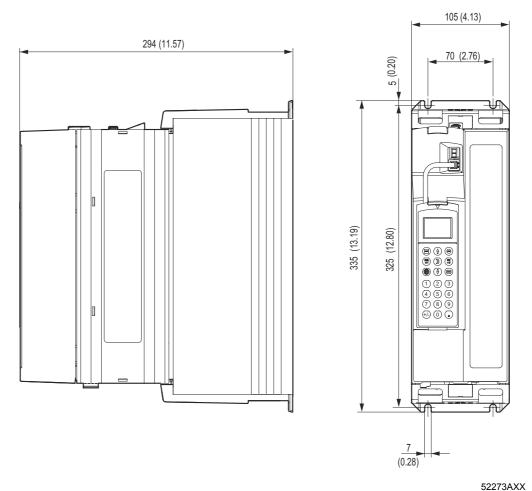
Dimensões MDX61B, tamanho 2S, dimensões em mm (in)
